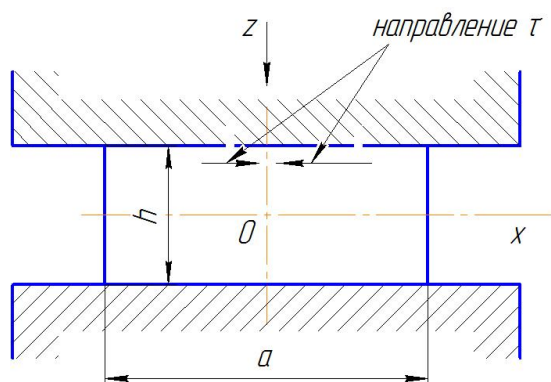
Расчетная схема:  $h$  – начальная высота заготовки;  $a$  – ширина заготовки
